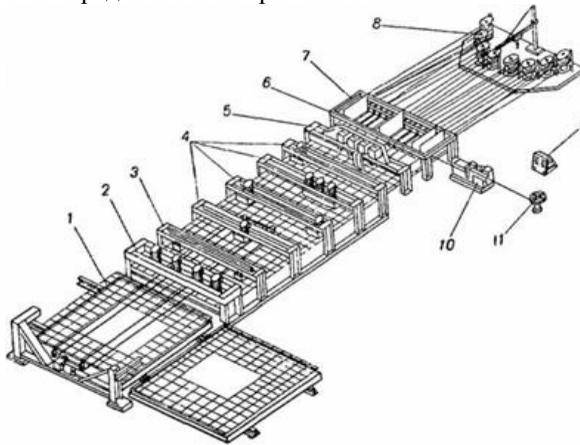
Автоматизированная линия для сварки широких сеток:
